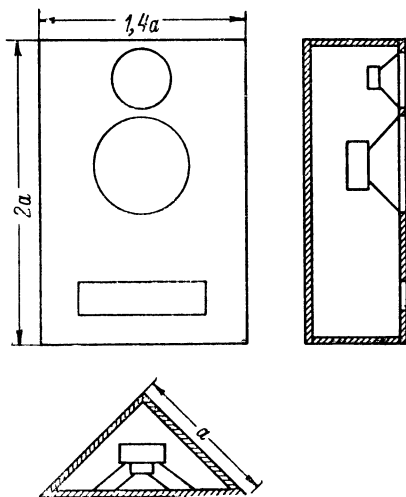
Конструкция и размеры призматического фазоинвертора, предназначенного для размещения в углу комнаты.
